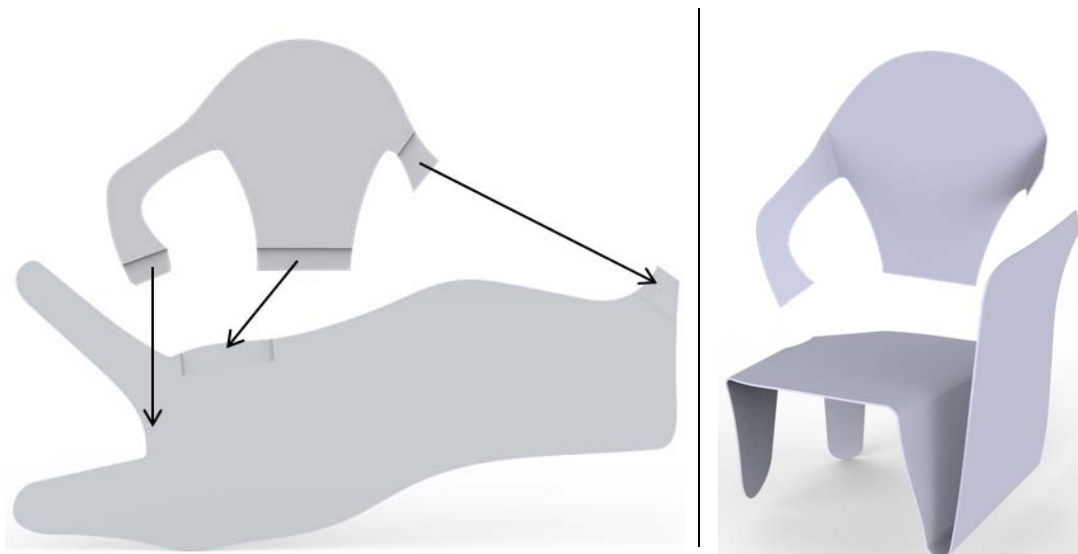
Esquema de proposta de dobragem e união através da planificação 2D da cadeira
